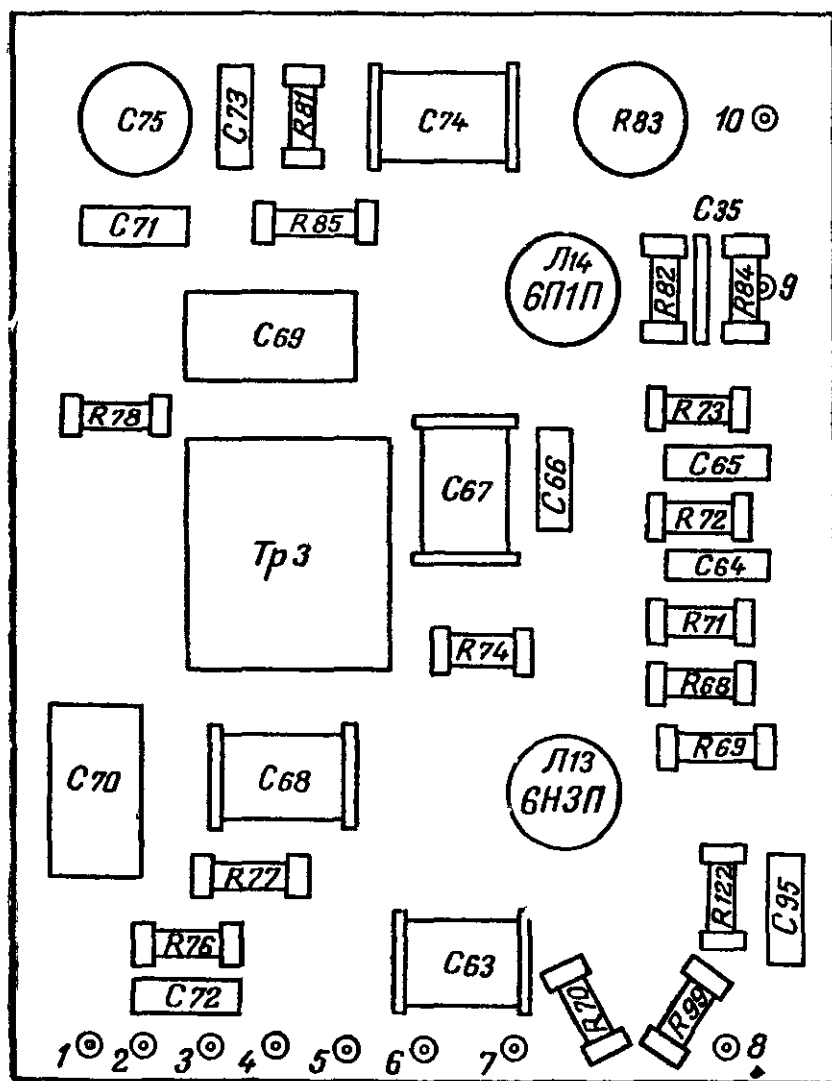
Расположение деталей на плате кадровой развертки телевизора «Старт».
